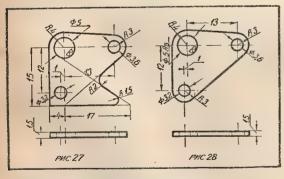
Щечка собачки рычагов Рис. 28. Щечка собачки рычагов
